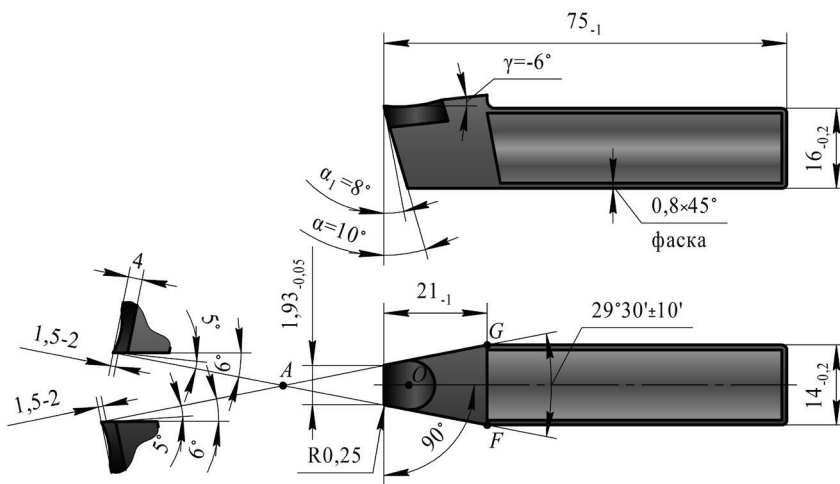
Конструкция резца для оснащения охватывающей фрезы
